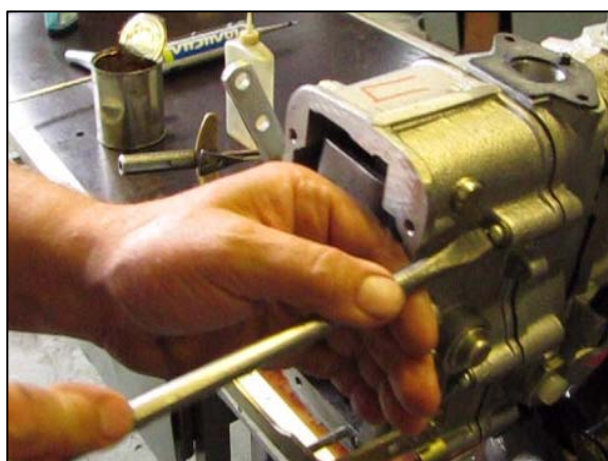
Затяжка болтов крепления крышки регулятора
